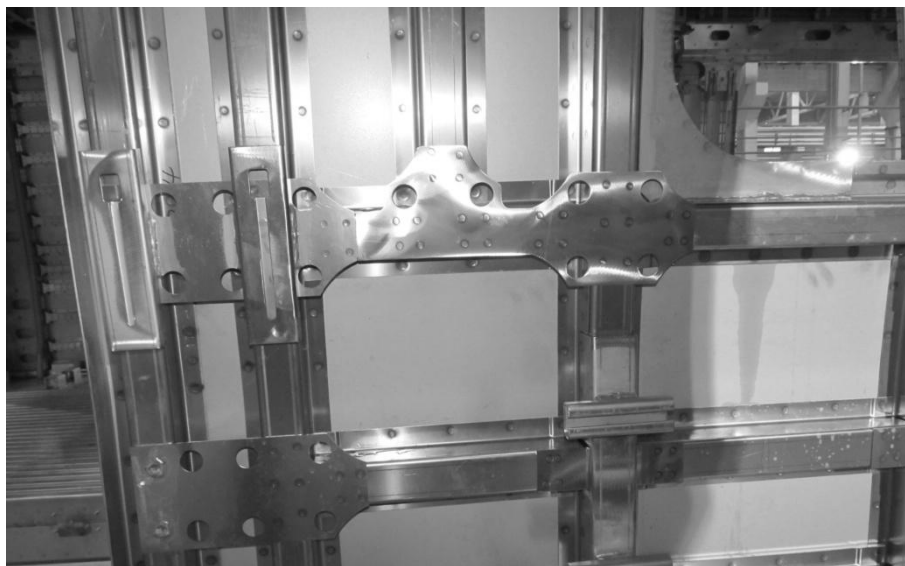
Місця розташування типових зварних з'єднань у внутрішній частині вагону швидкісного потягу
